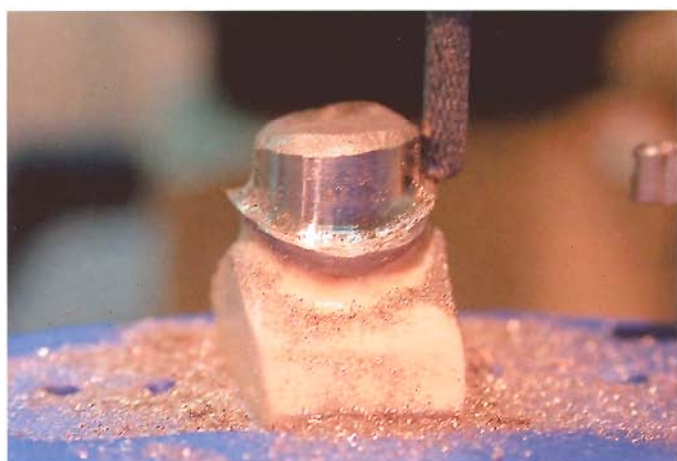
Am Fräsgerät werden die Oberflächen nachgefräst.
